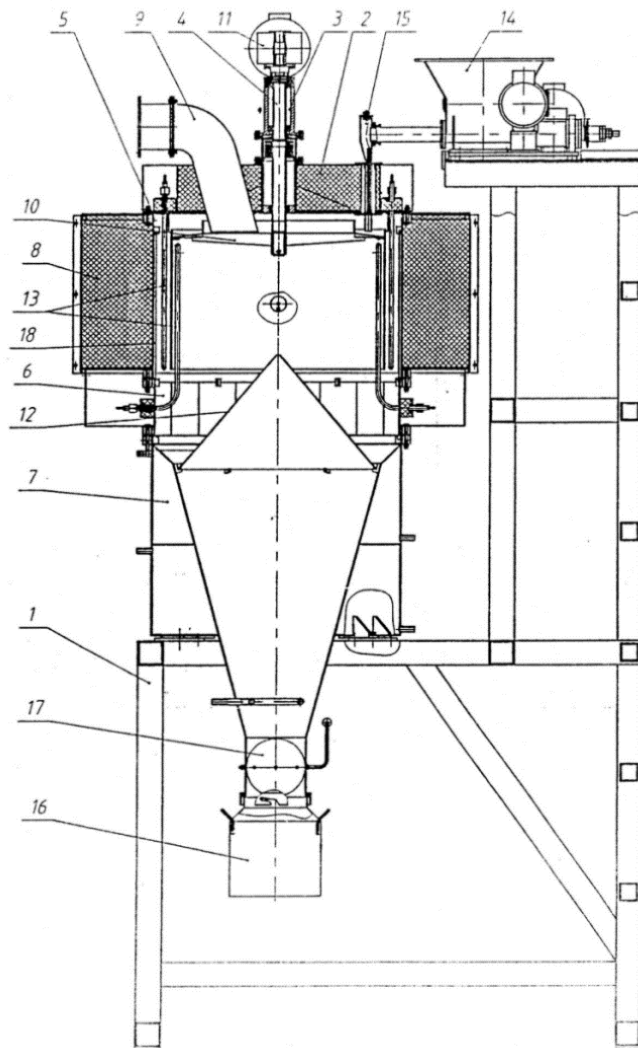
Опытно-промышленный центробежной реактор барабанного типа ЦЕФЛАР™: 1 – рама; 2 – крышка; 3 – подшипниковая опора; 4 – вал; 5 – корпус; 6 – проставка; 7 – холодильник; 8 – кожух; 9 – воздуховод; 10 – барабан; 11 – привод; 12 – конус; 13 – ТЭНы; 14 – питатель; 15 – лоток; 16 – емкость; 17 – заслонка; 18 – экран
